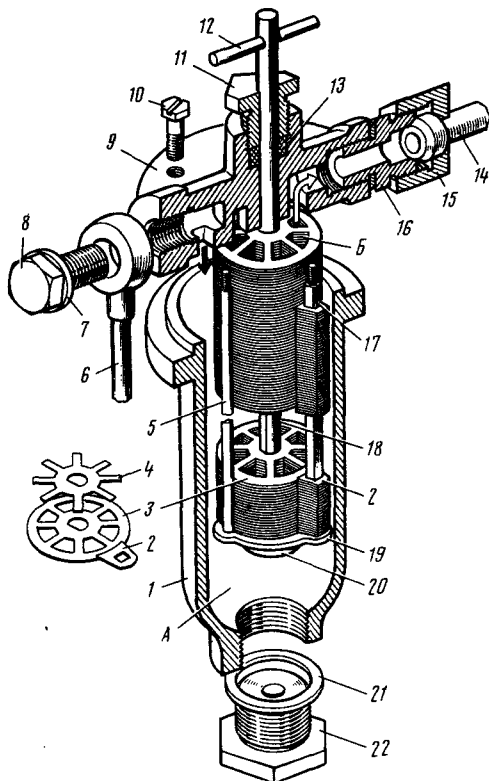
Топливный фильтр грубой очистки: 1 — корпус; 2 — нож; 3, 4 — рабочие и промежуточные пластины; 5 — направляющий стержень; 6, 14 — трубопроводы подвода и отвода топлива; 7, 21 — уплотнительные кольца; 8, 16 — штуцера; 9 — крышка; 10 — винт; 11, 22 — пробки; 12 — рукоятка; 13 — сальник; 15 — накидная гайка; 17 — квадратный стержень; 18 — центральный стержень; 19 — фигурная шайба; 20 — диск; А, Б — полости неочищенного и очищенного топлива
